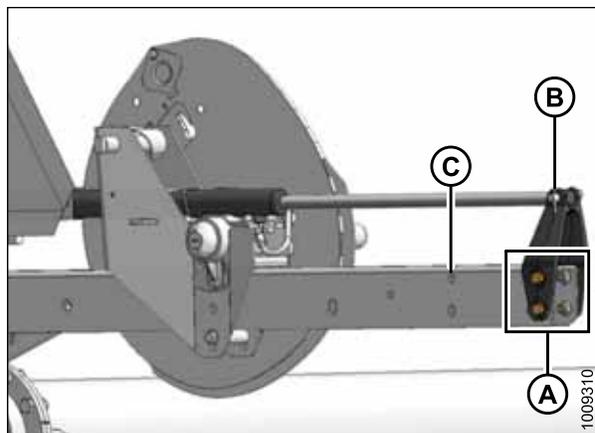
Цилиндр правого рычага мотовила в переднем положении
